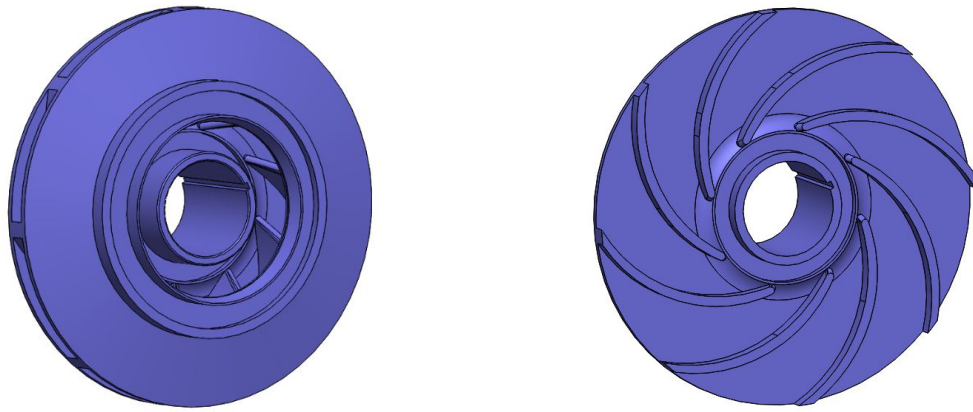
Общий вид и разрез рабочего колеса ЭЦН
